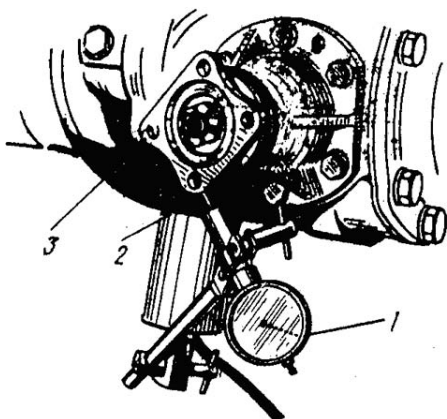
Проверка бокового зазора между зубьями шестерен главной передачи переднего ведущего моста. 1 — индикатор; 2 — штوك приспособления; 3 — фланец стакана ведущей шестерни.
